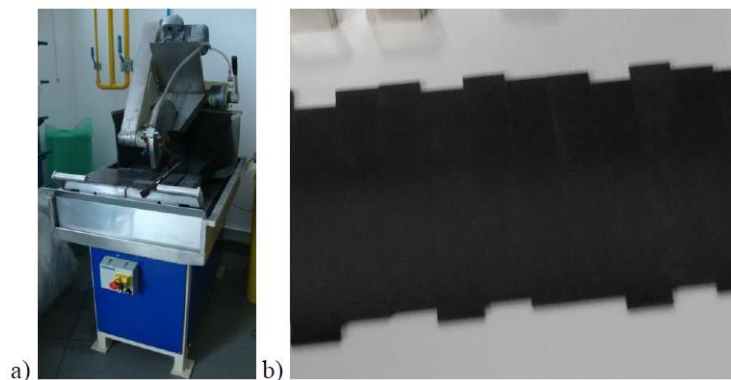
a) Máquina de corte e b) provetes cortados [3].
